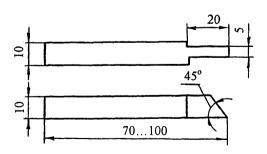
Боек для изготовления искусственных дефектов типа зарубок
